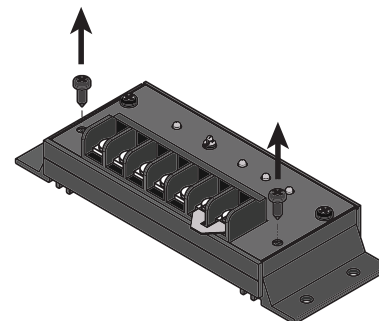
Entfernen der 2 Schrauben der Blende.
